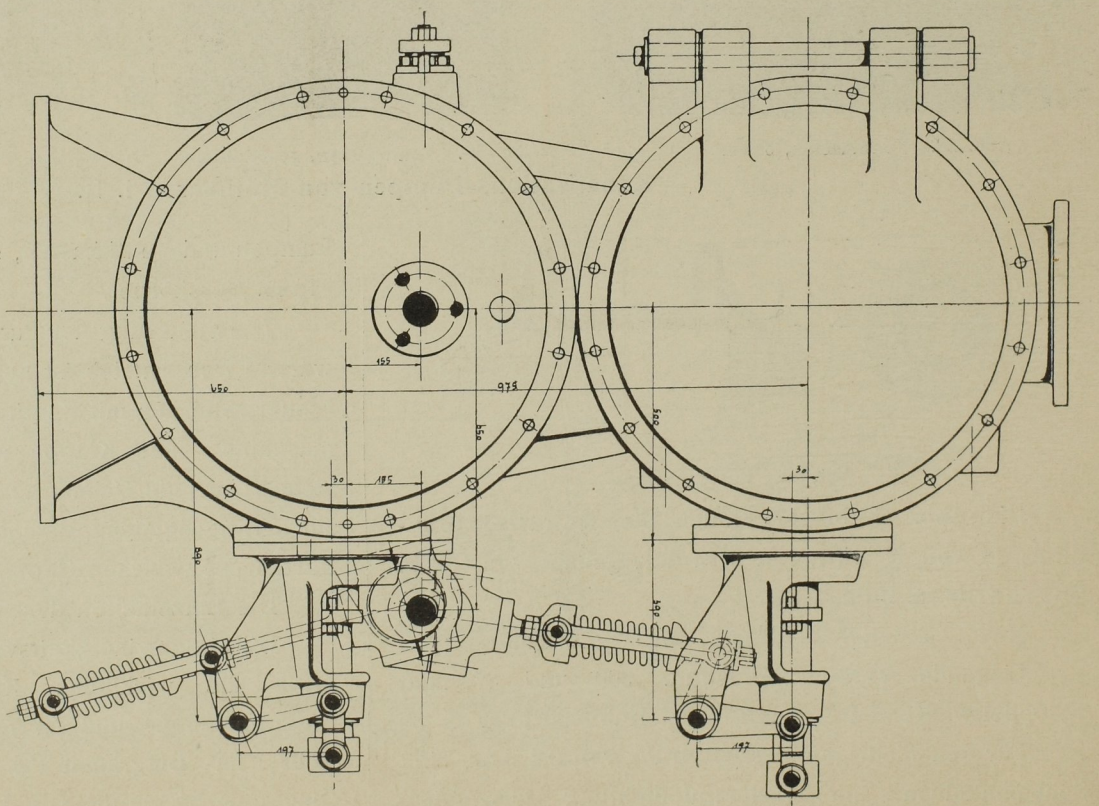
Stirnansicht der Pumpe mit Steuerung. Massst. 1:15.
